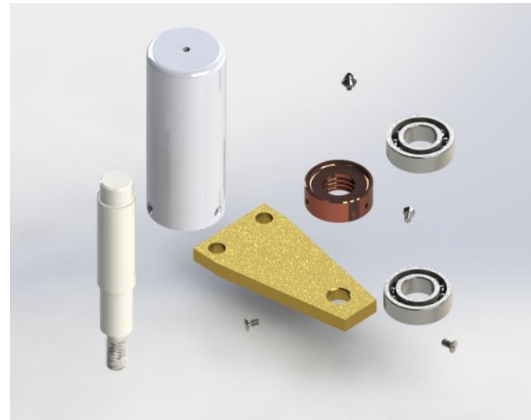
Presentación visual explosionada de la unidad ensamblada.
